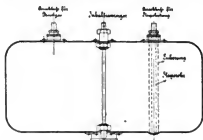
Explosions-sicherer Benzintank der „Feg“ in Salzkotten.
